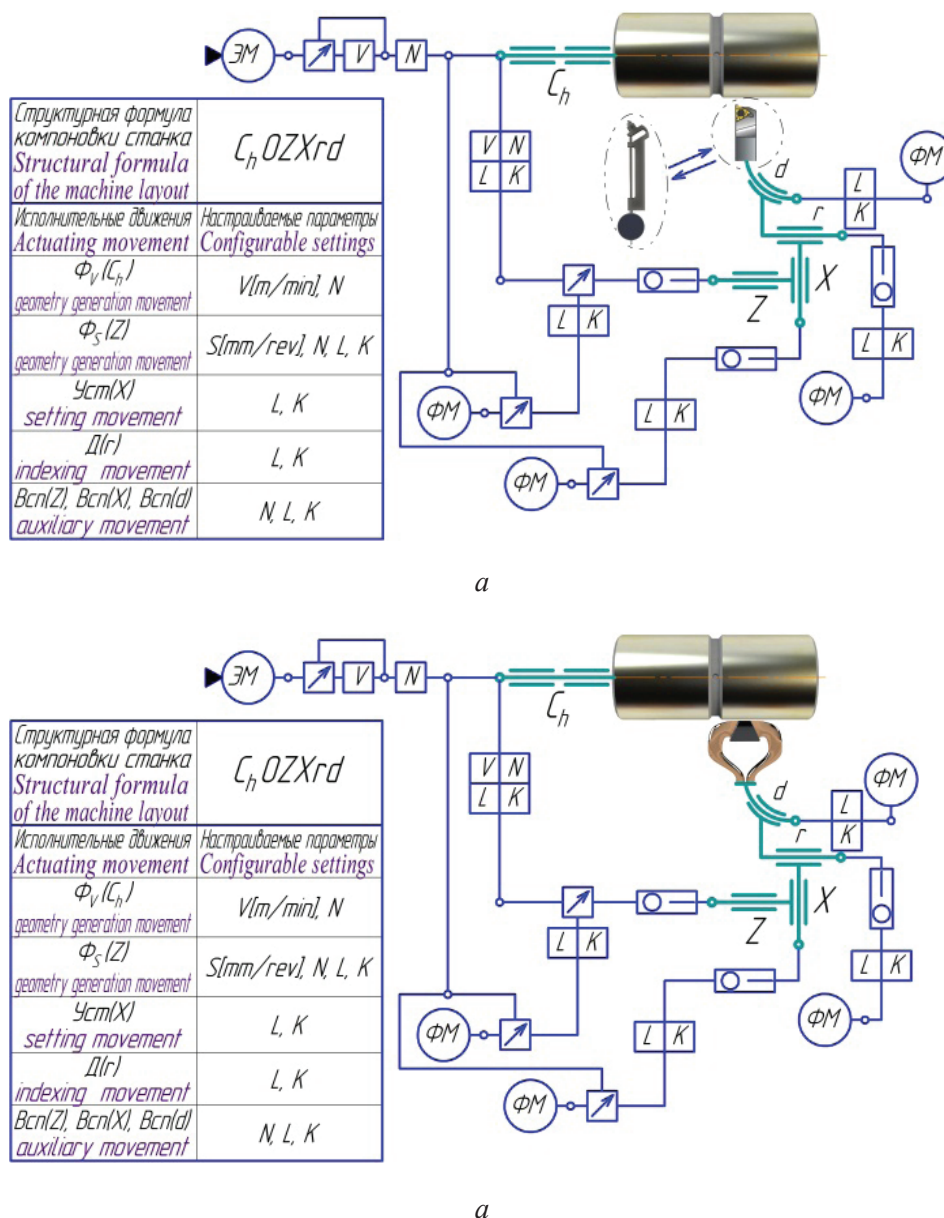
Структурно-кинематические схемы при обработке цилиндрической поверхности:
